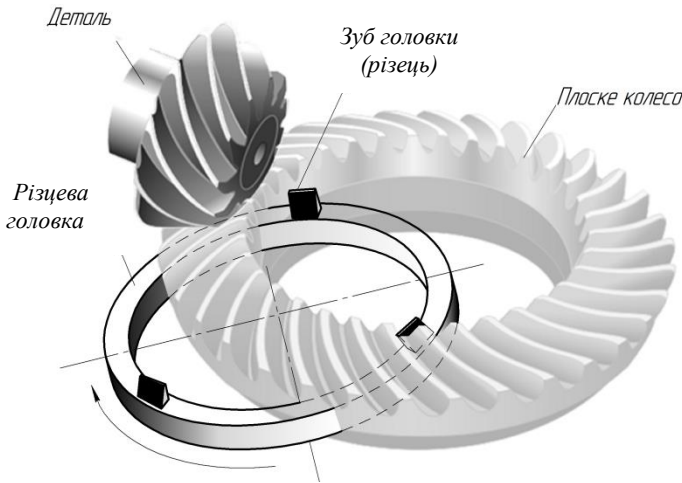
Схема нарізування конічних коліс із коловими зубами
